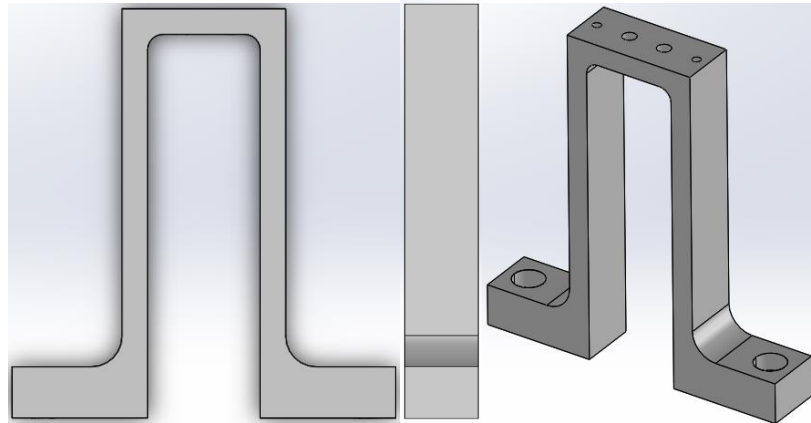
Držák hořáku vyrobený konvenčními technologiemi
